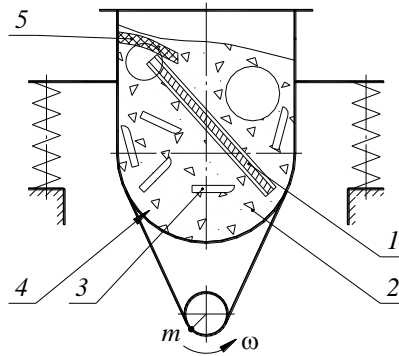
Схема обробки деталей «в навал» з орієнтуванням їх переміщення охоплюючою поверхнею резервуара: 1 – охоплююча поверхня – перегородка; 2 – резервуар; 3 – деталі, що обробляються; 4 – абразивний наповнювач; 5 – кожух
